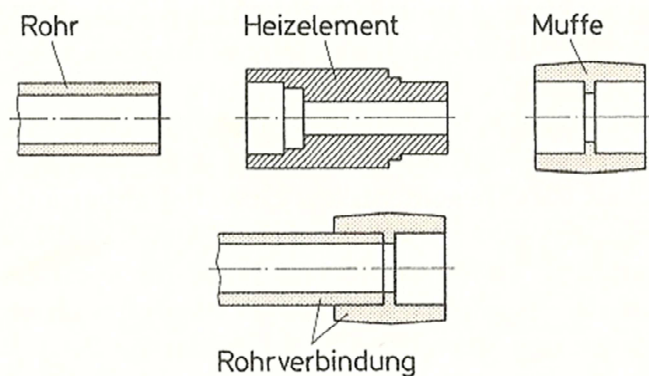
Prinzip Hezelementmuffenschweißen
